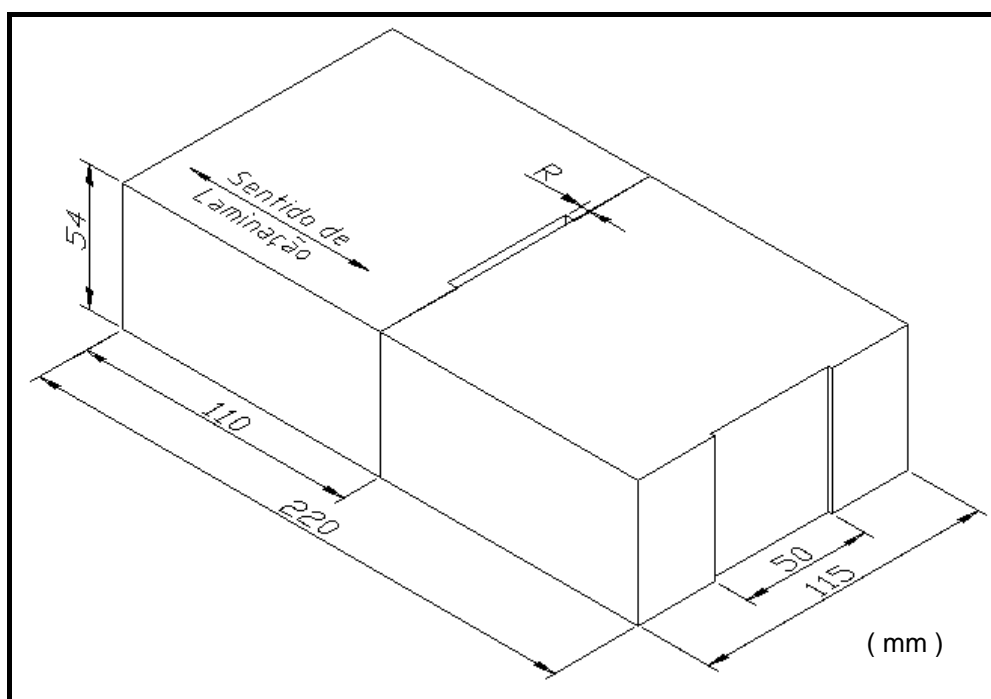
Dimensões em mm do corpo de prova G-BOP. Adaptado de McParlan e Graville⁽⁹⁾.
